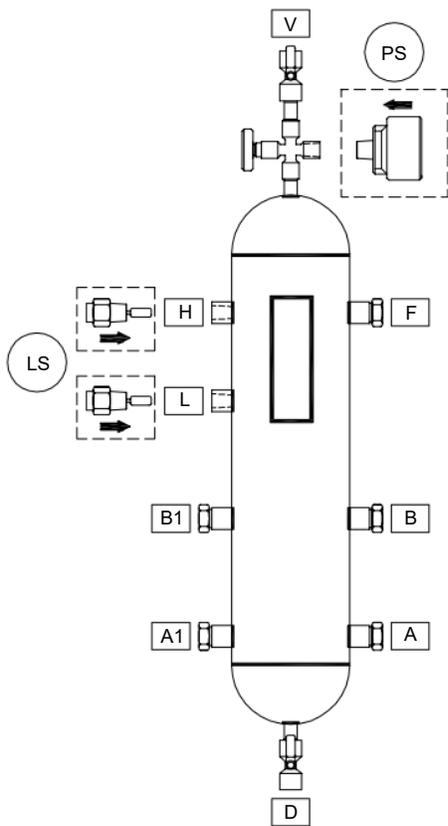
Montaje de interruptores del Plano 53A de tuberías
